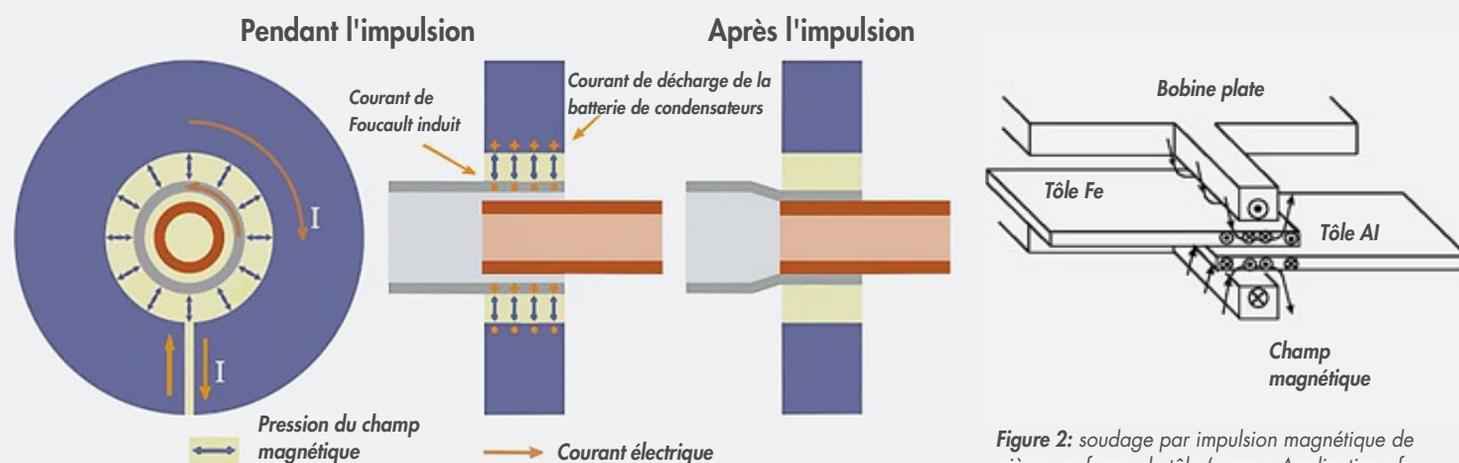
soudage par impulsion magnétique de pièces en forme de tôle (source: Application of magnetic pulse welding for aluminium alloys and SPCC steel sheet joints. T. Aizawa et al)
